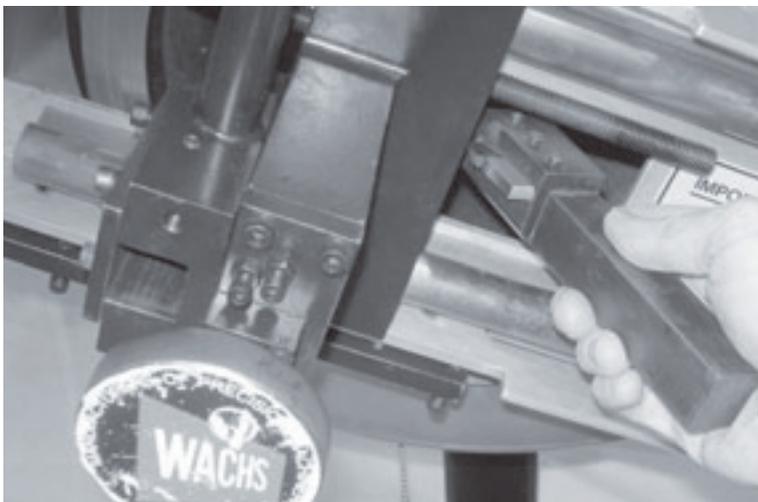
Lösen Sie die Schrauben auf der Werkzeughalterplatte, damit der Werkzeughalter in den Werkzeugschlitten eingepasst werden kann.
